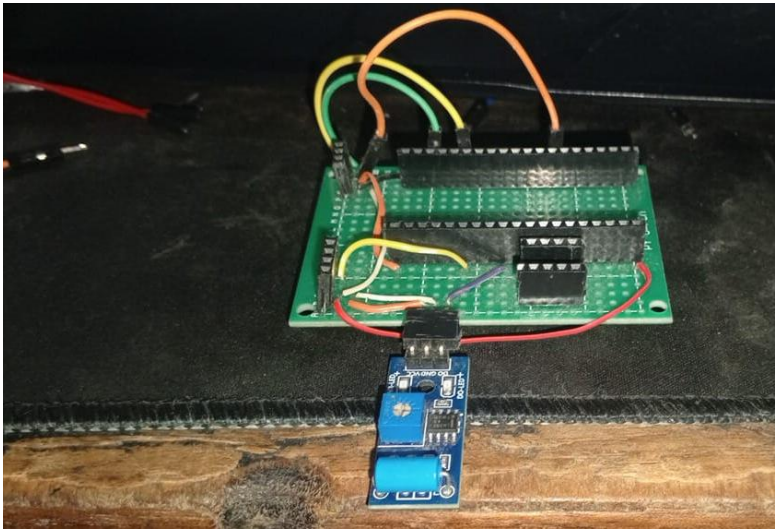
Preparación de la protoboard y soldadura de pines header.
